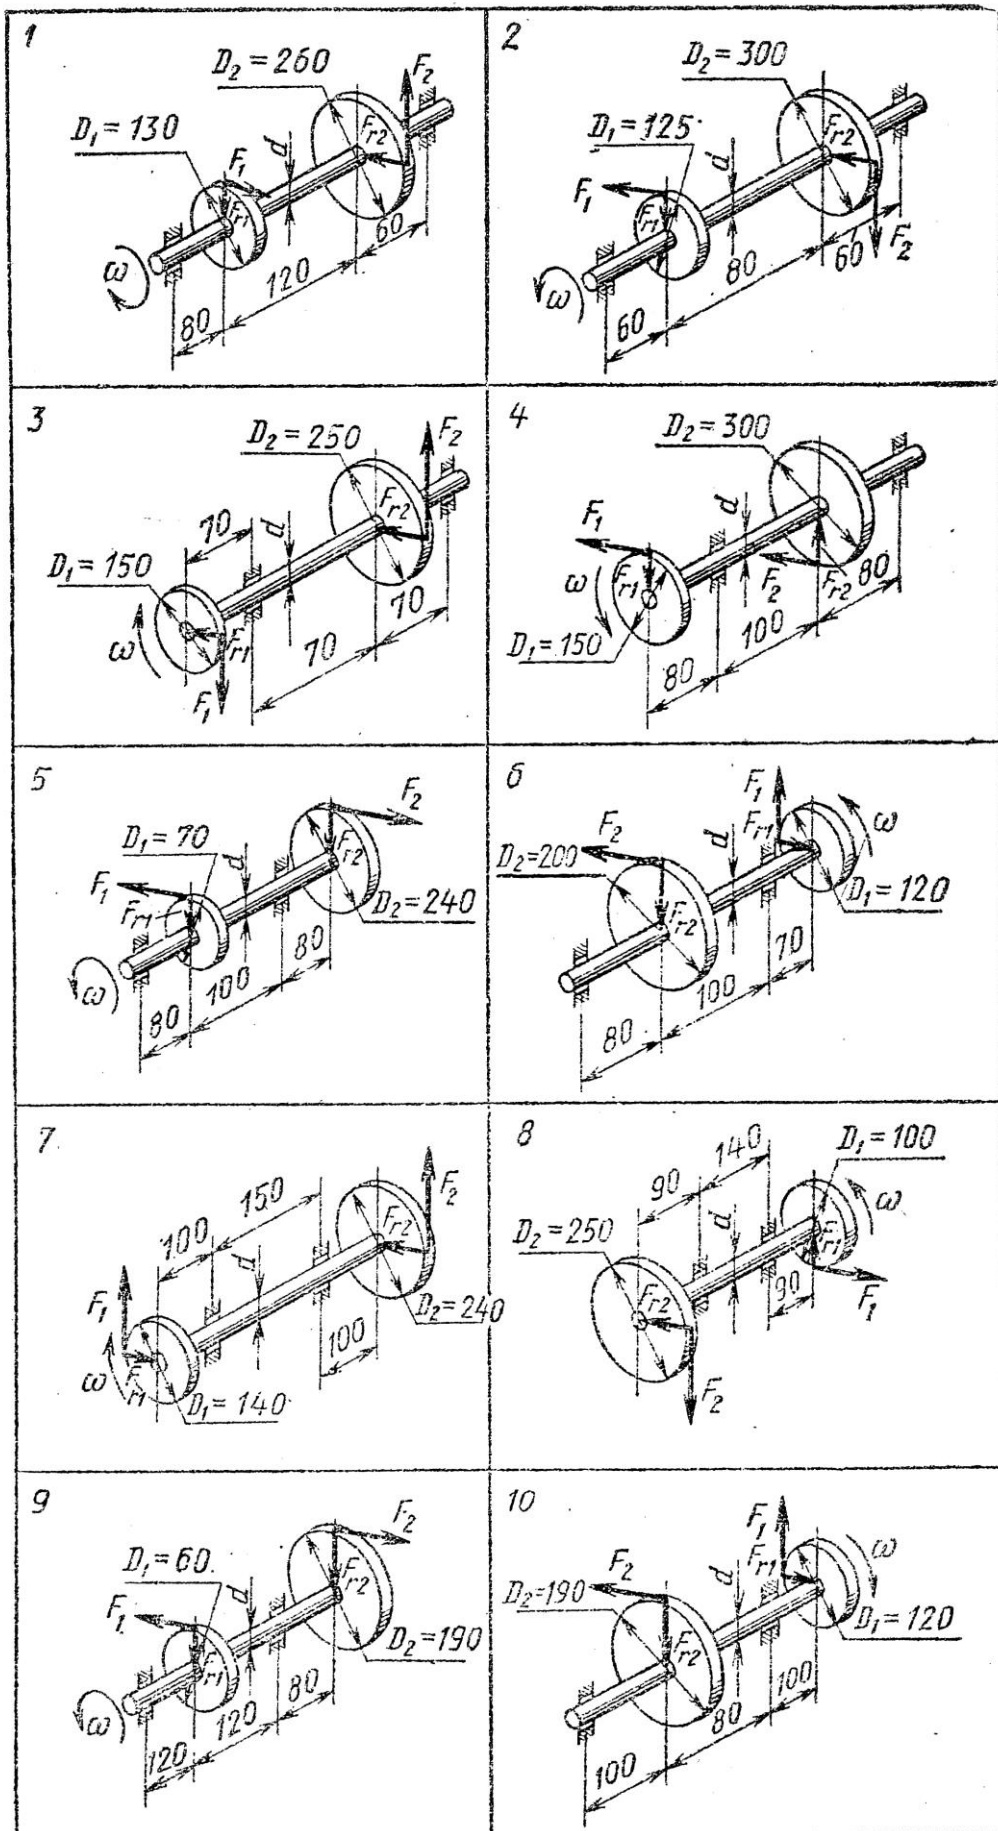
Стальной вал с двумя зубчатыми колесами
